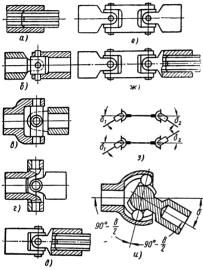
Подвижные муфты: a — раздвижная втулочная; δ — малогабаритная шарнирная асинхронная; ϵ — крупногабаритная шарнирная асинхронная с целой крестовиной; ϵ — то же, но с разъемным кольцом; ϵ — шарнирно-раздвижная; ϵ — сдвоенная шарнирно-раздвижная (универсальный карнирно-раздвижная (универсальный кардан); ϵ — схемы расположения осей валов и шарниров в сдвоенных муфтах, обеспечивающие получение синхронной передачи вращения; ϵ — шарнирная синхронная муфта
